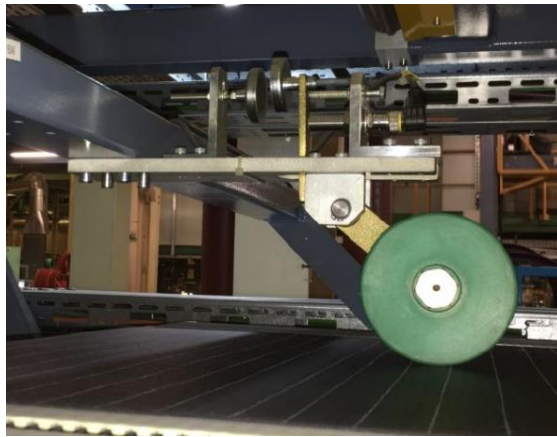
Mecanismo de deteção usado nas máquinas de construção.
